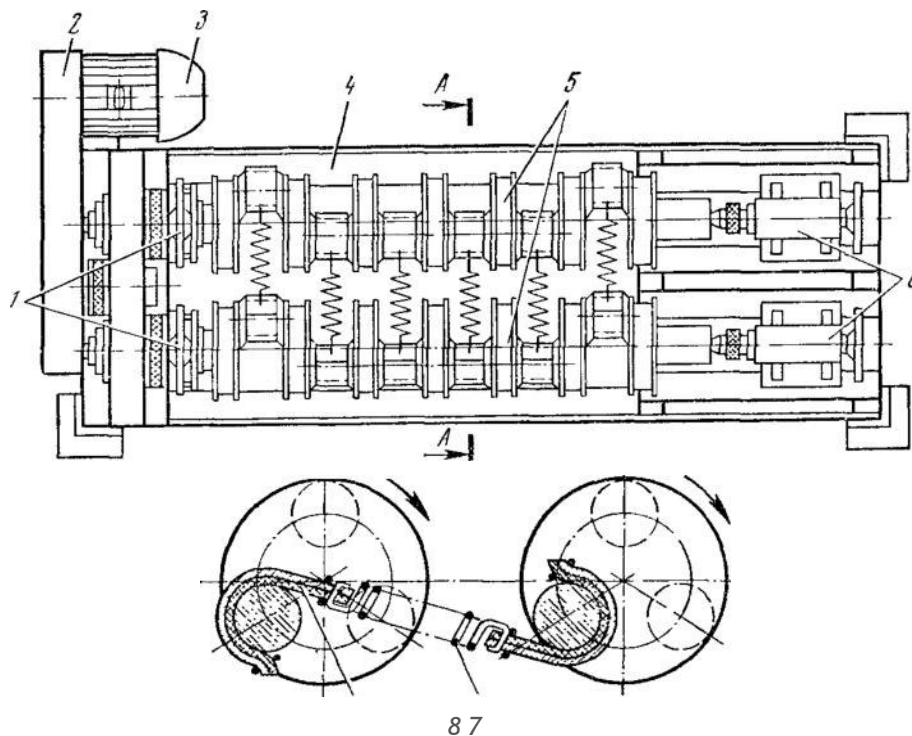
Схема станка для полирования шеек коленчатого вала:
